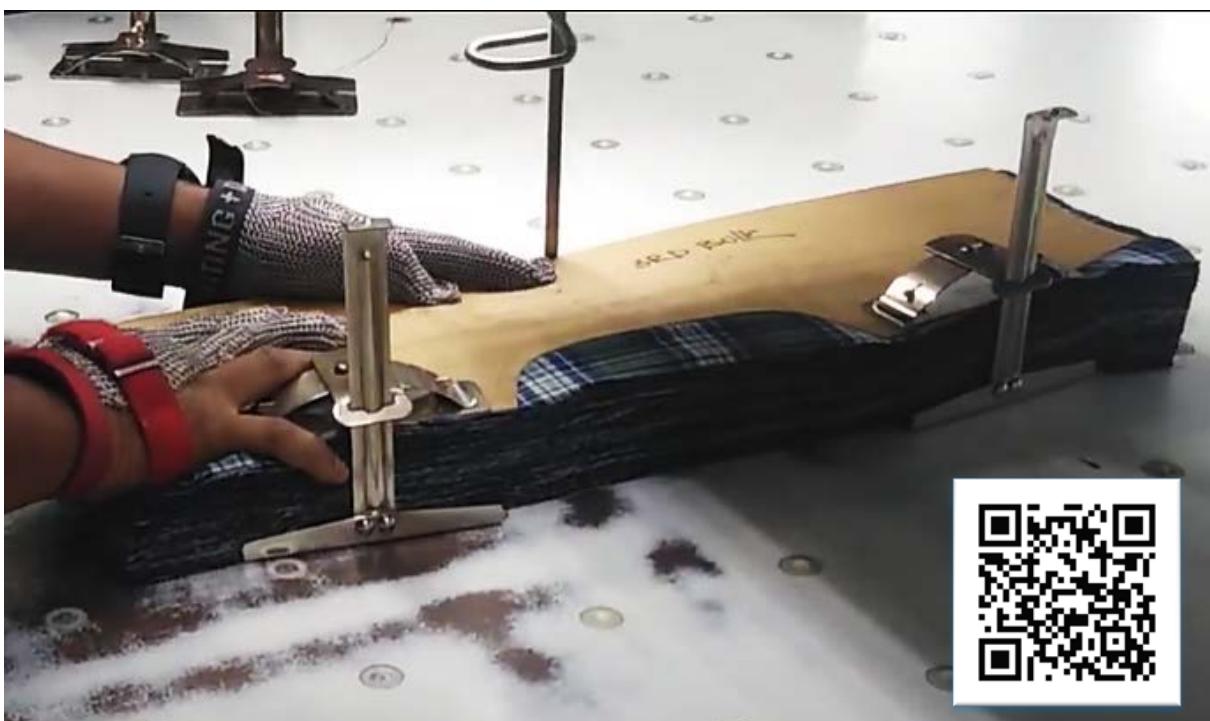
Використання лекала для розкрою деталей (<https://youtu.be/IFeS5KDEF4U>)
